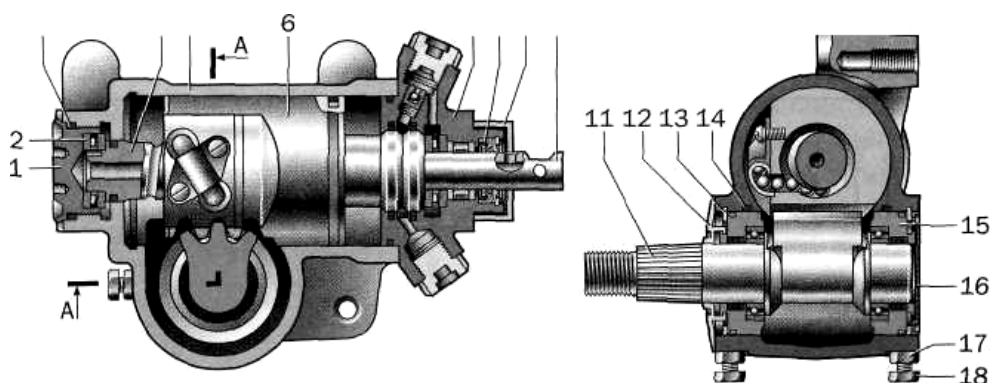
Рулевой механизм типа «винт-шариковая гайка-рейка-зубчатый сектор» без гидроусилителя (а): 1 — картер; 2 — винт с шариковой гайкой; 3 — вал-сектор; 4 — пробка заливного отверстия; 5 — регулировочные прокладки; 6 — вал; 7 — уплотнитель рулевого вала; 8 — сошка; 9 — крышка; 10 — уплотнитель вала-сектора; 11 — наружное кольцо подшипника вала-сектора; 12 — стопорное кольцо; 13 — уплотнительное кольцо; 14 — боковая крышка; 15 — пробка;
